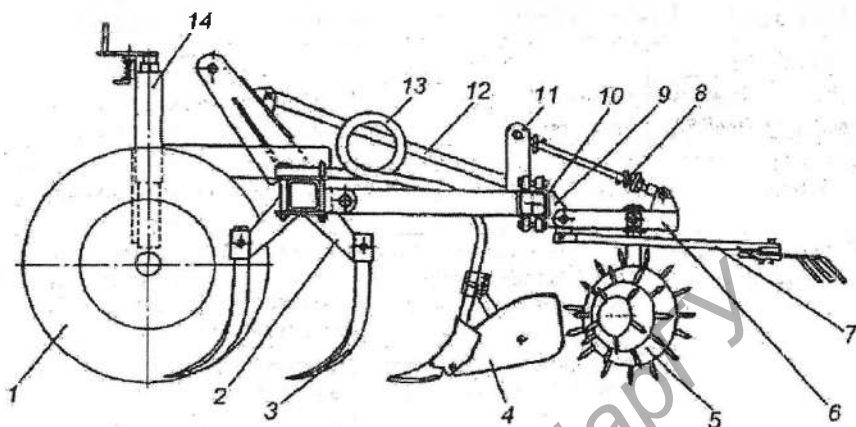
Культиватор-окучник-гребнеобразователь ОКГ-4 (вид сбоку):
